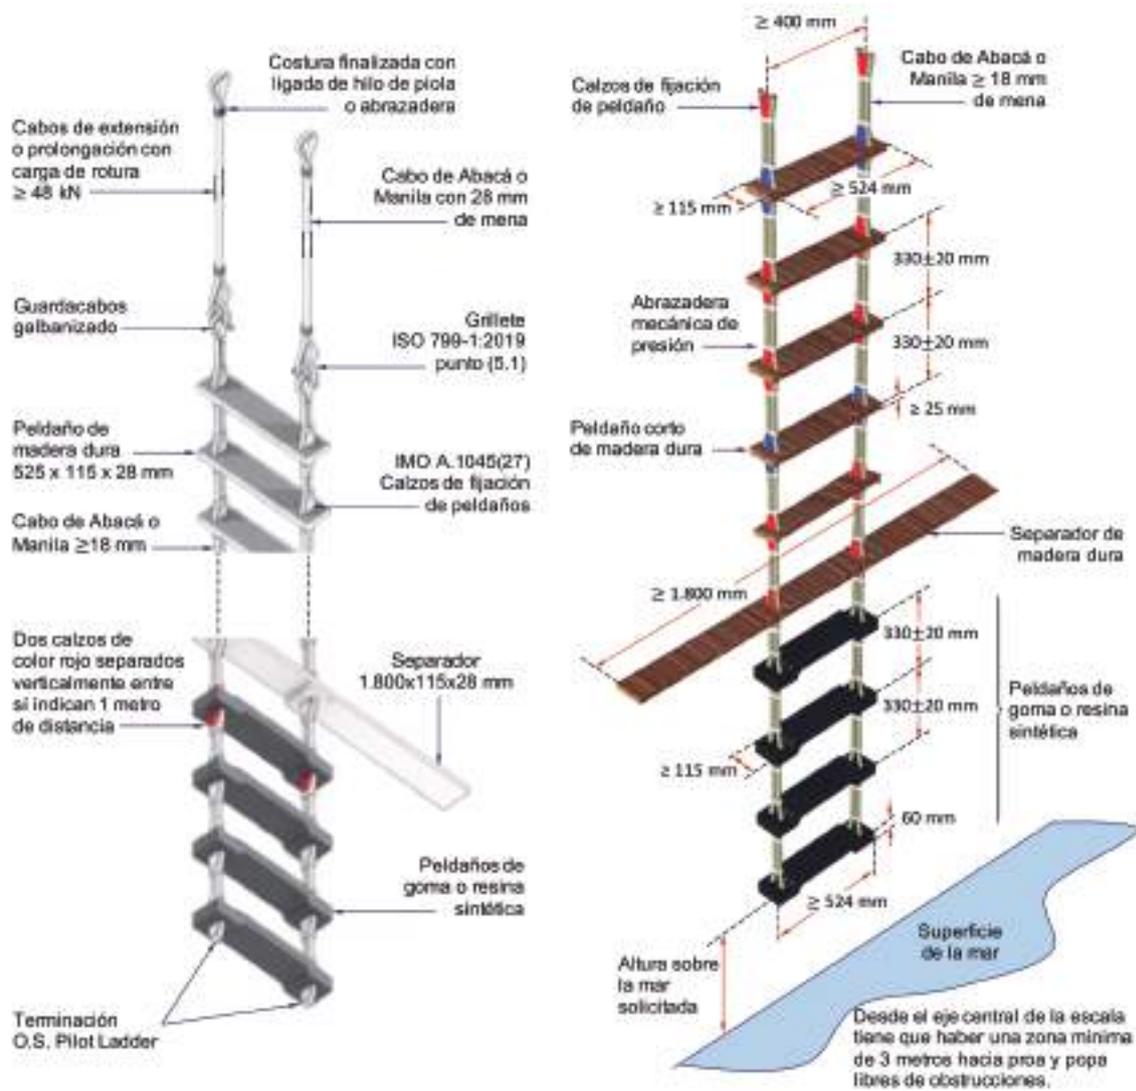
Dimensiones y partes principales de una escala de práctico.
